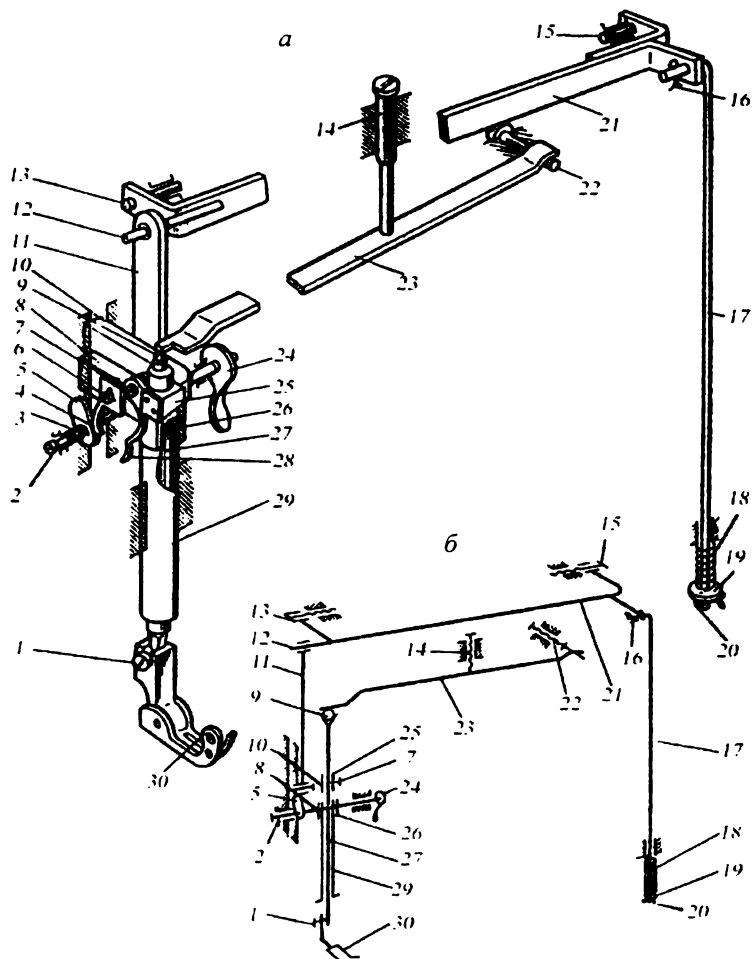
Механизм движения лапки машины 97-А кл. ОЗЛМ
